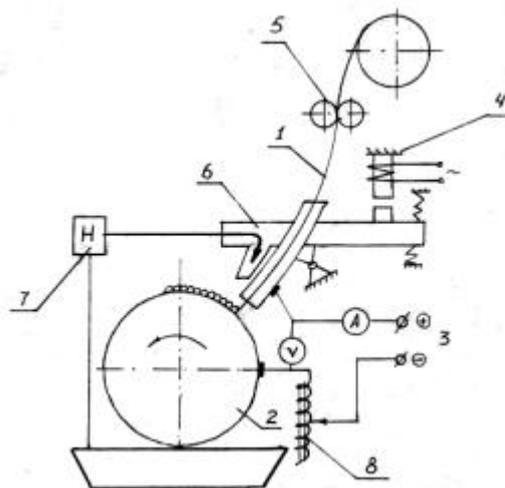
Схема вибродуговой наплавки: 1 – электродная проволока, 2 – деталь, 3 – источник постоянного тока, 4 – электромагнитный вибратор, 5 – механизм подачи проволоки, 6 – охлаждающая жидкость, 7 – насос, 8 – катушка самоиндукции
